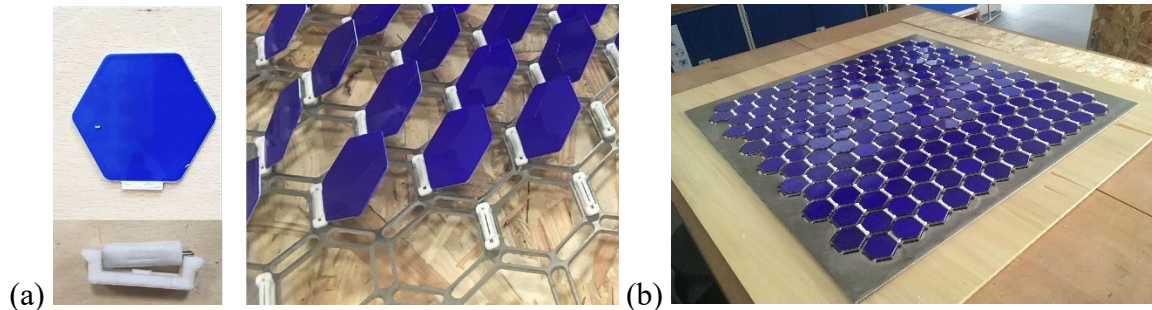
(a) Montage du prototype STEGOS, (b) Prototype final.
